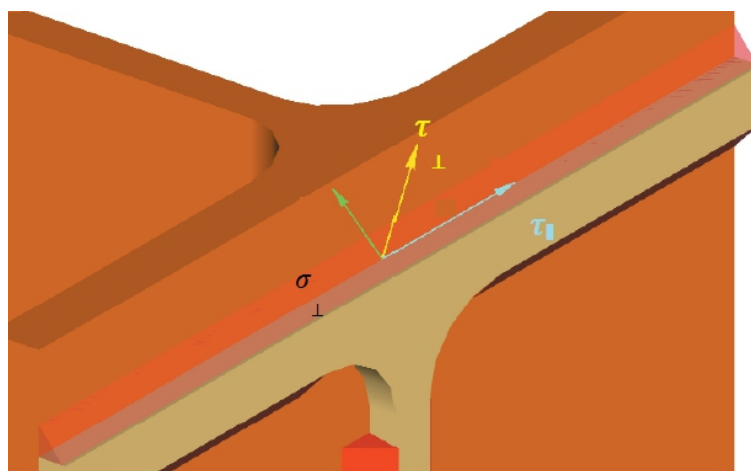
Descomposición de los esfuerzos transmitidos al cordón de soldadura
